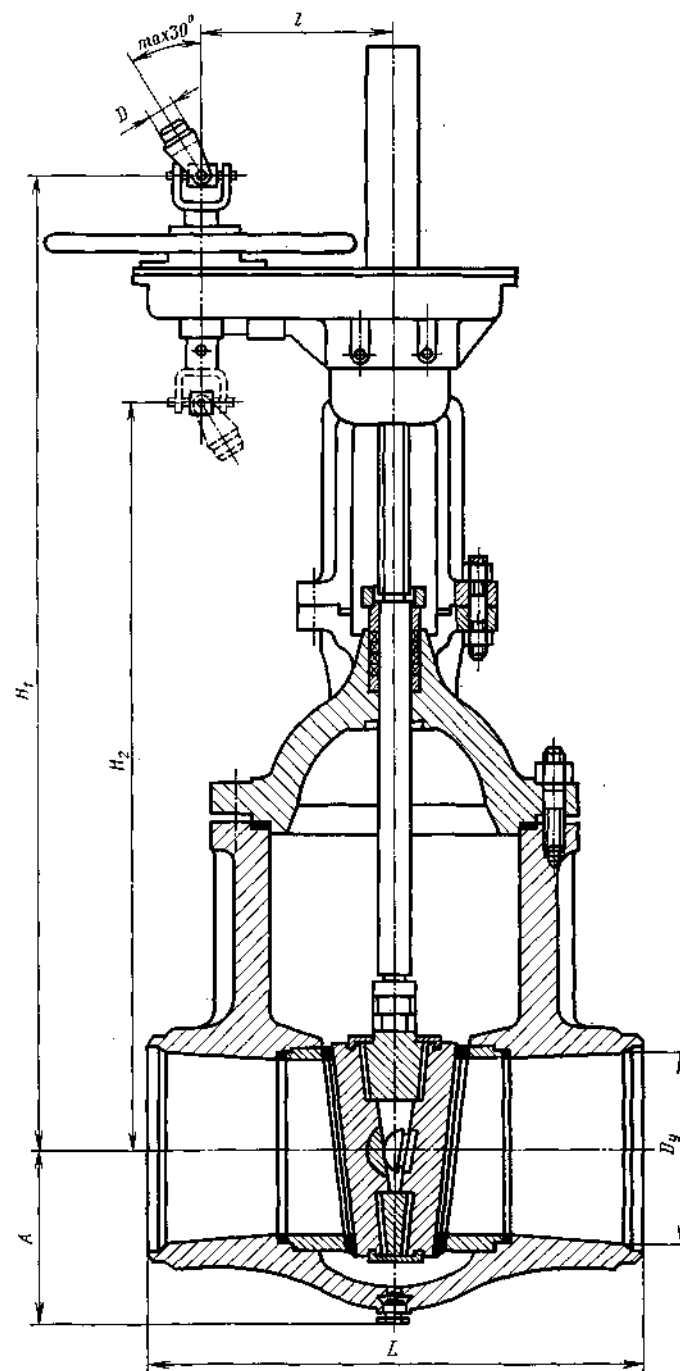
Задвижка с приводной головкой с цилиндрическим зубчатым редуктором Ду, 350, 400 и 450 серии 850
